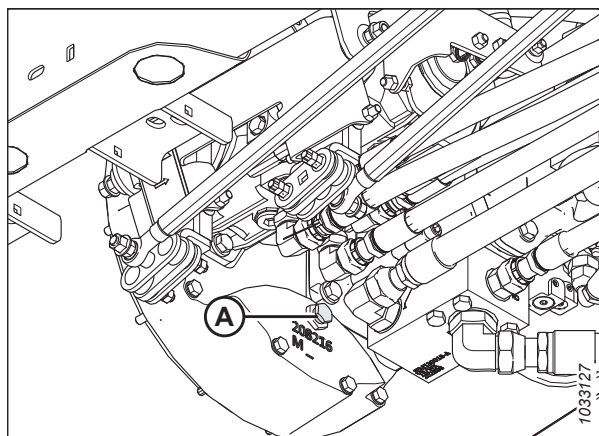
Пробка отверстия для контроля масла редуктора
